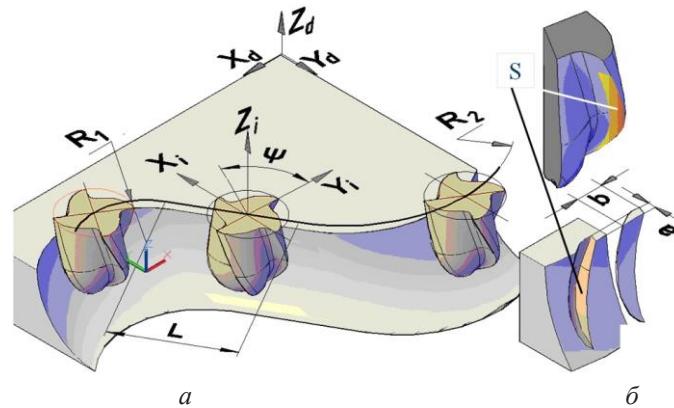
3D макет процесса фрезерования концевой радиусной фрезой
